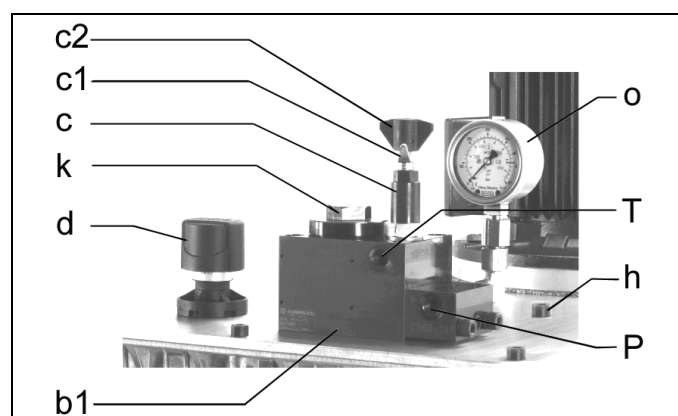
Groupe hydraulique avec bloque de connexion et filtre haute pression
